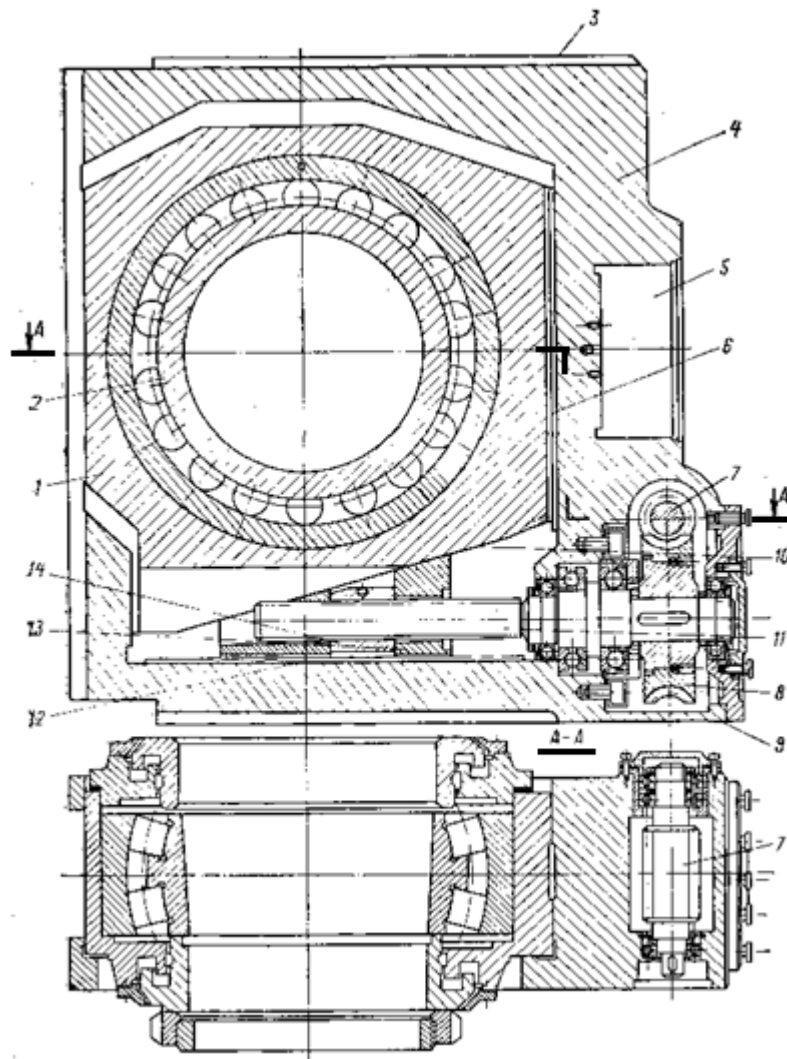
Підшипниковий вузол валка каландра з механізмом перекоосу:
